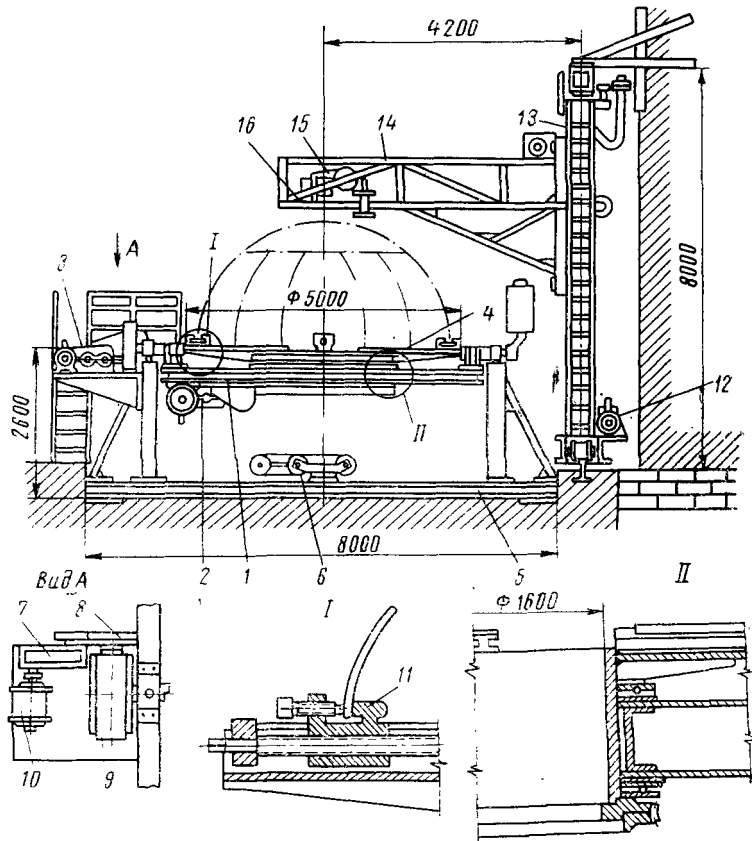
Установка для автоматической сварки полусферических днищ
